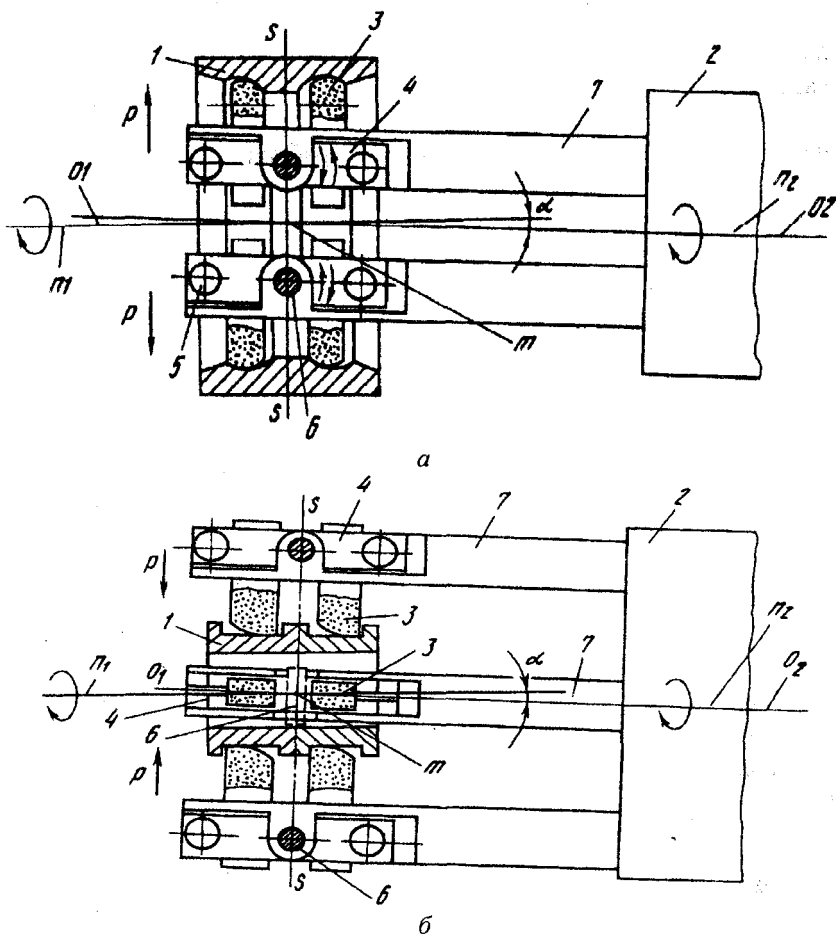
Способ чистовой обработки колец двухрядных подшипников
